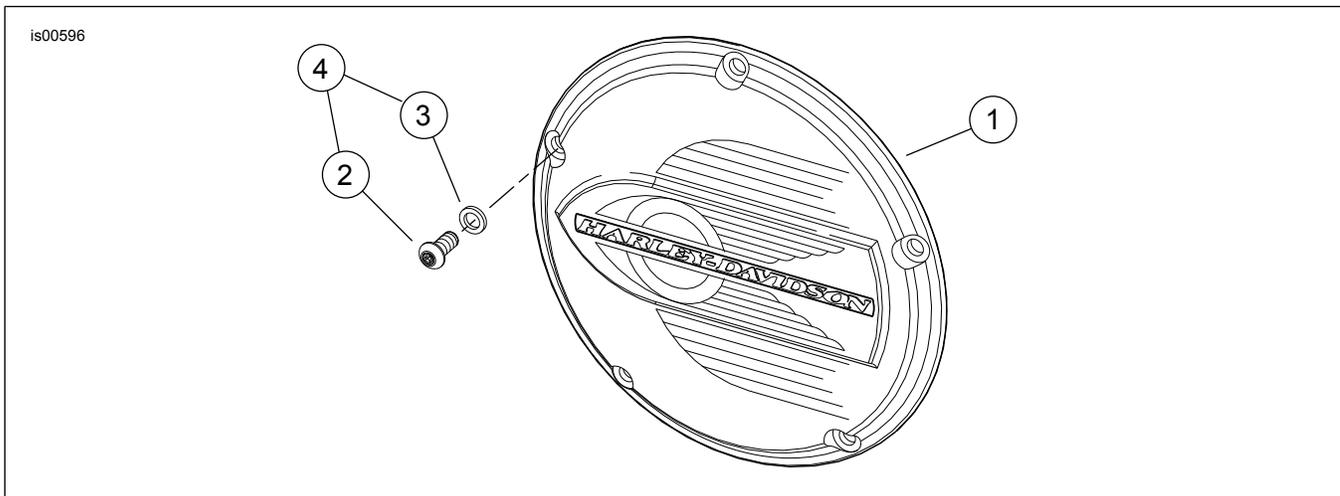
Tampa de inspeção da embreagem "Flying Wheel"
